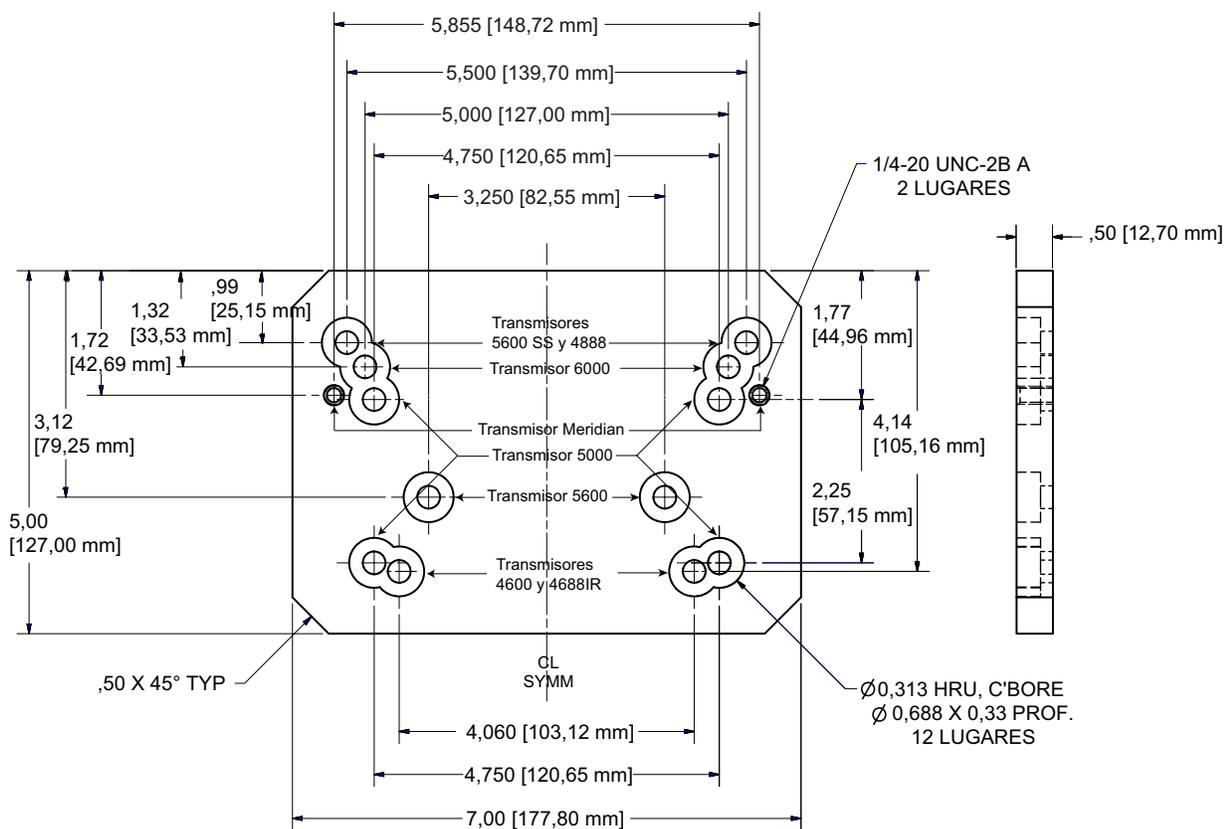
Dimensiones de la placa de montaje de adaptación - Aluminio
